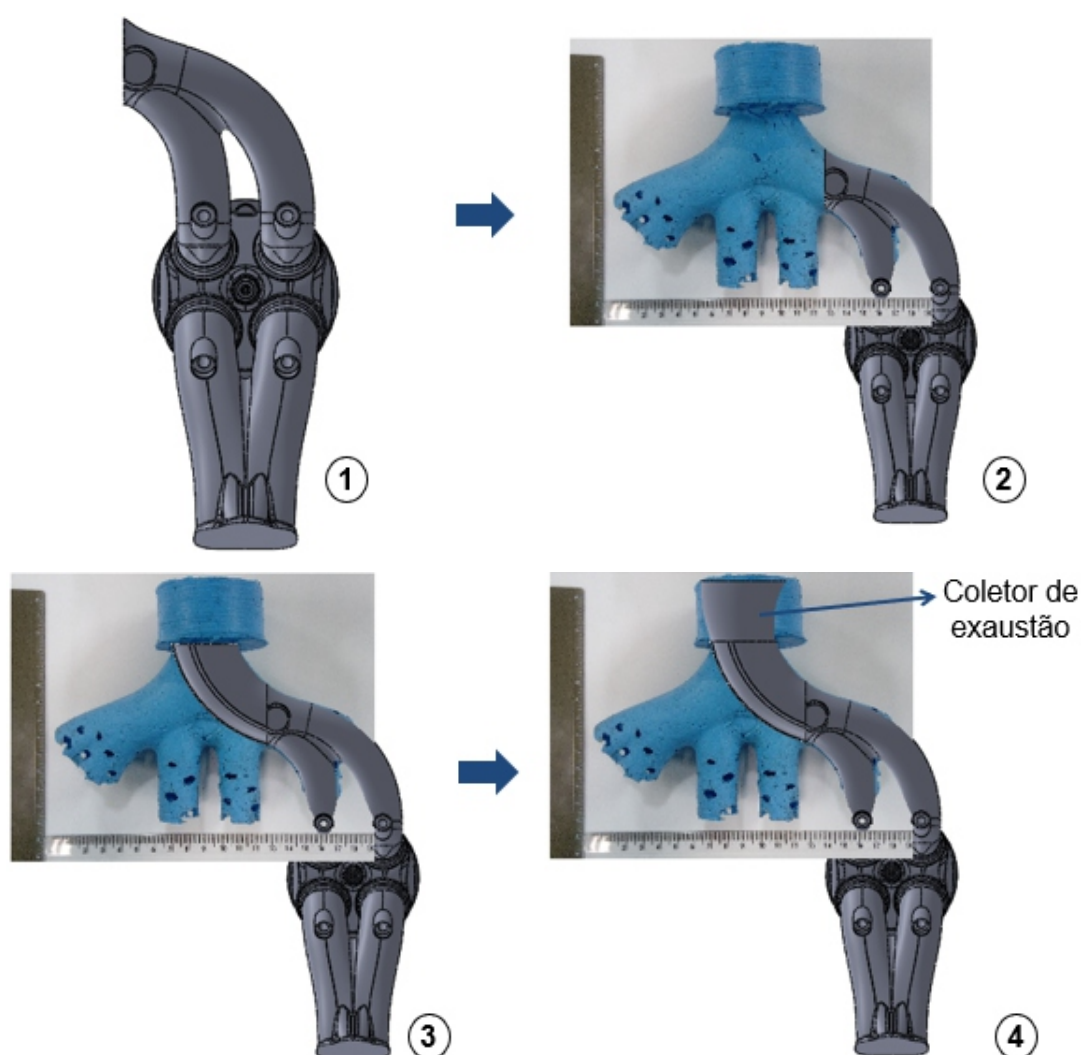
Molde do pÓrtico de exaustão obtido por meio da tÓcnica de moldagem com silicone.
